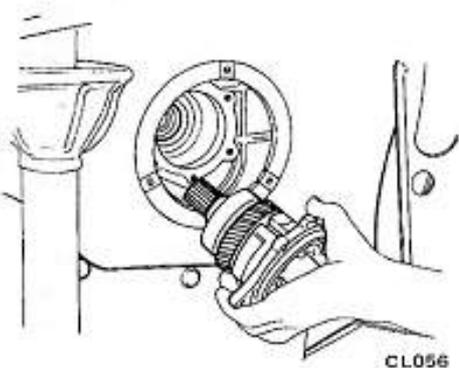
Dépose du pignon récepteur d'entrée assemblé
